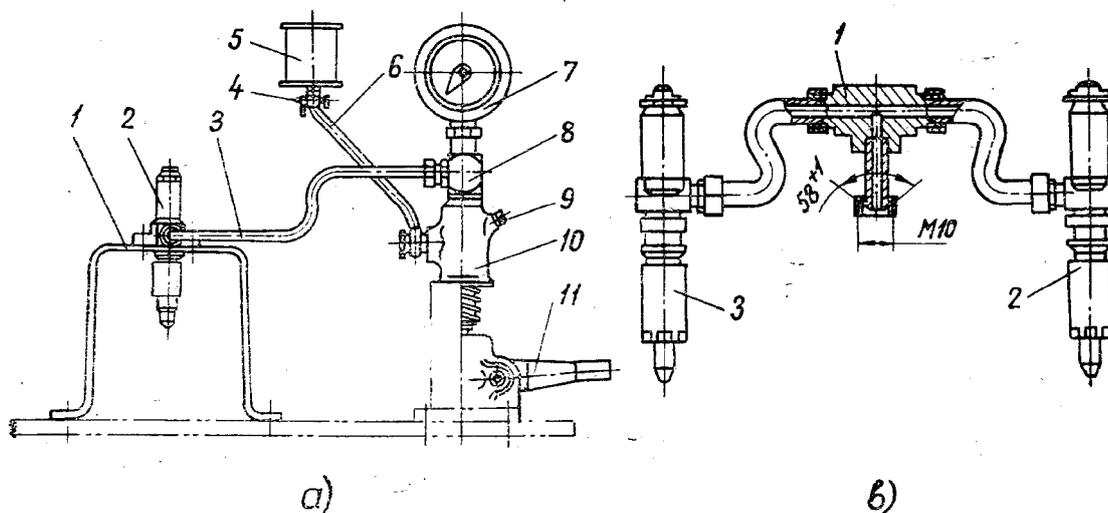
Схемы установки приспособлений для проверки форсунок:
